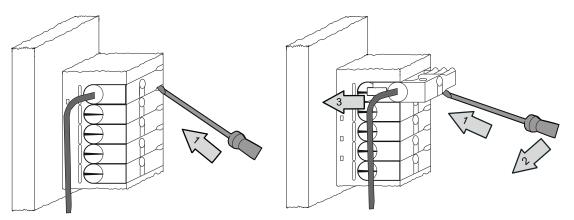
Déconnexion d'un câblage d'un connecteur Fast Connect à 20 points
